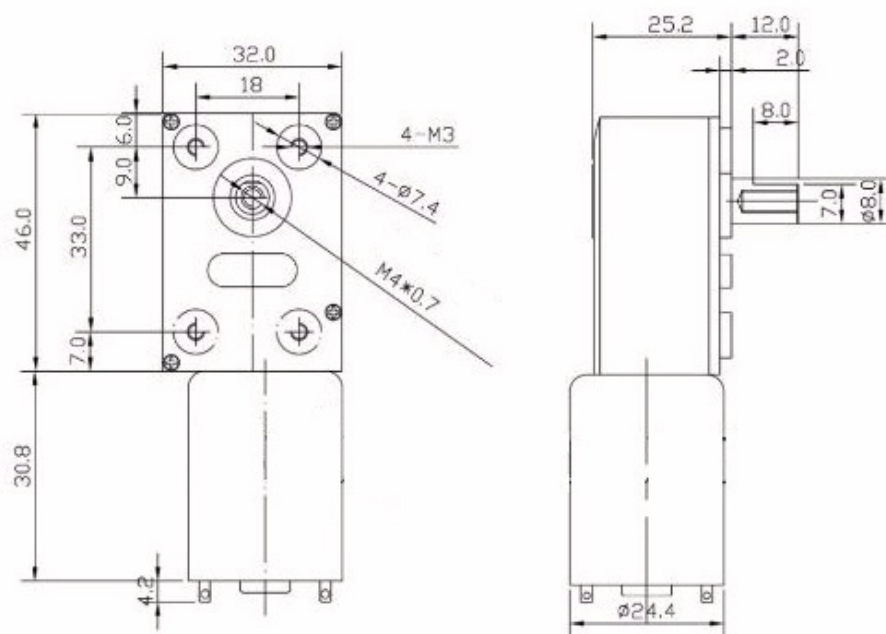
Disegno CAD del motoriduttore DC da 12V
